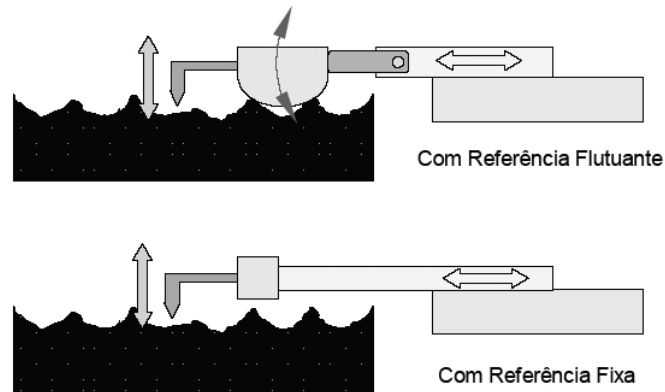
Princípio de operação de rugosímetros com apalpador mecânico
